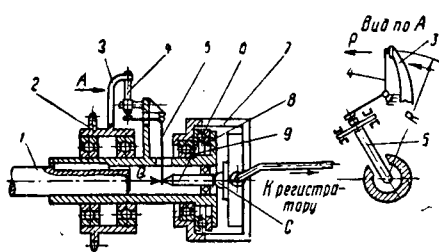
Схема гидравлического динамометра стороны к цилиндрам присоединены трубки 6, соединяющие их с просверленным в валу 1 отверстием. В вал ввёрнута деталь 7 с просверленными осевыми и радиальными отверстиями. На ней свободно посажен невращающийся корпус сальника, соединённый с манометром 8 и ручным компенсационным насосом 9. Гидравлическая система заливается маслом.
